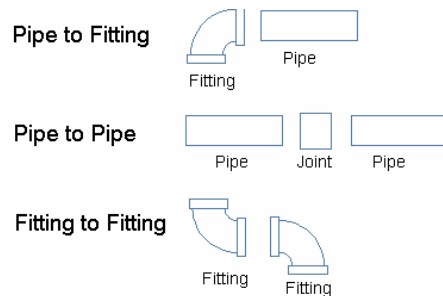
Assemblage par raccord emmanché-soudé, brasé, à extrémités collées, à brasure tendre, fileté, forgé, capillaire et à souder
